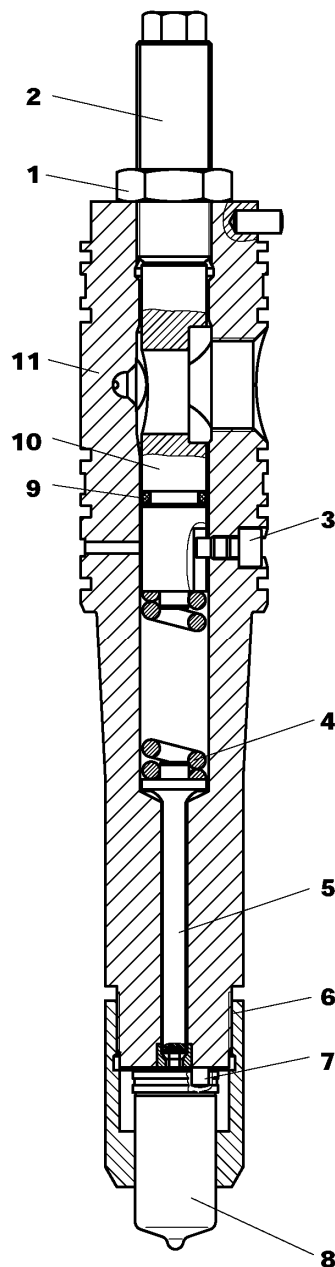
Штатна форсунка дизеля МаК М43С охолоджувана маслом: 1 – контргайка; 2 – регулювальний стакан; 3 – підведення палива; 4 – пружина; 5 – шток; 6 – накидна гайка; 7 – проставка; 8 – розпилювач; 9 – гумове ущільнювальне кільце; 10 – упор з порожниною охолодження; 11 – корпус
